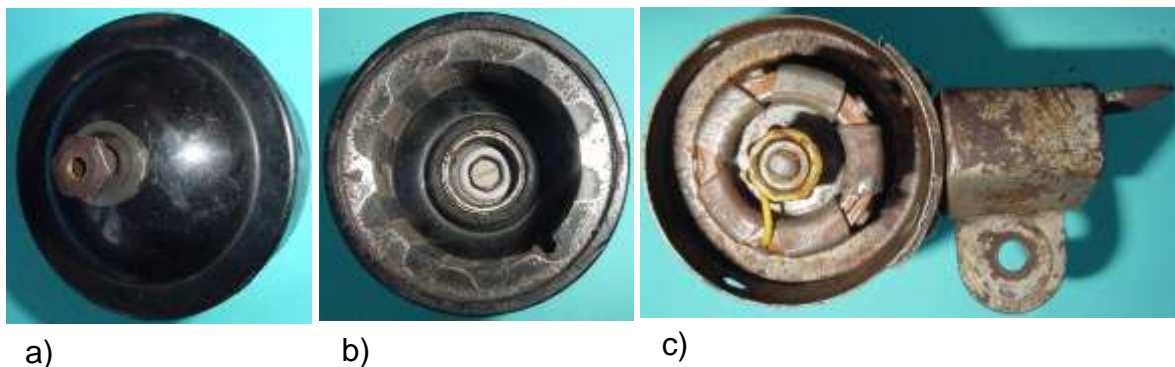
Baugruppen: a) Bodentopf aus Duroplast, b) Ständerbohrung, c) Lagerhals mit Klauenpolanker
